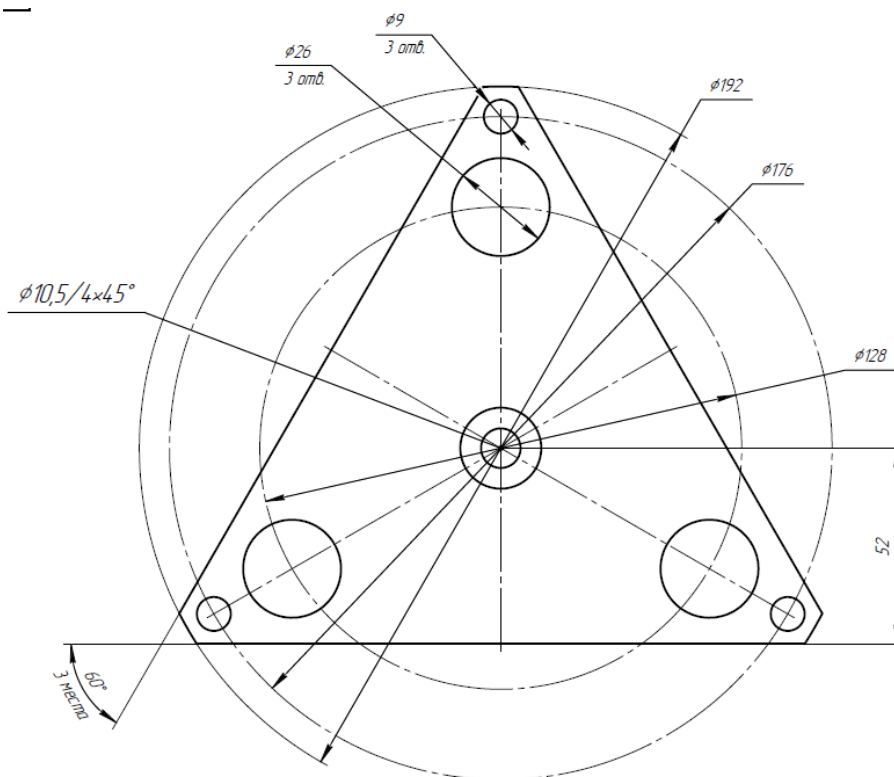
Присоединительные размеры детали «Пластина 2»
